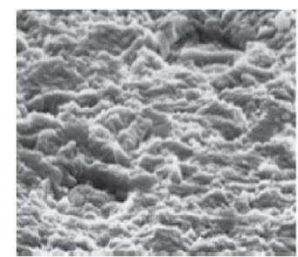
Mécanisme de défaillance des fils de bonding après cyclage thermique.
